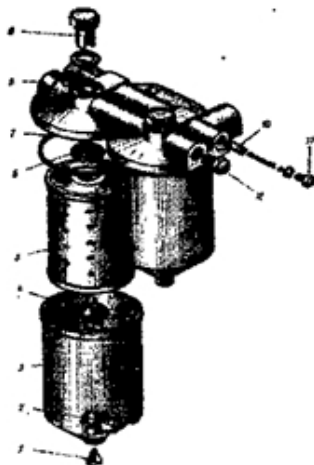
Фильтр тонкой очистки топлива: 1 - сливная пробка; 2 - стержень; 3 - стакан; 4,6,7- уплотнительные прокладки; 5 -фильтрующий элемент; 8 - корпус; 9,11, 12 -пробки; 10 - сливной клапан-жиклер.
